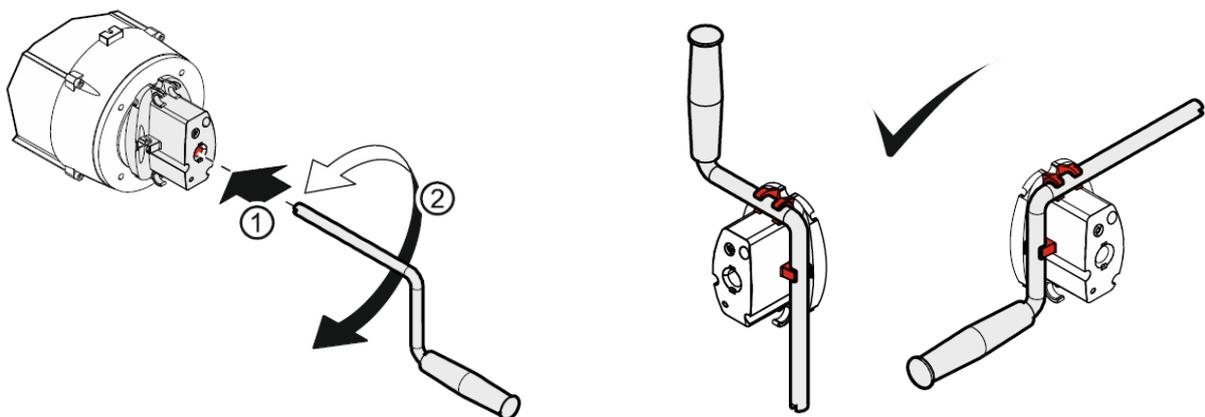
Detailskizze zum Entsperren mit Kurbel
